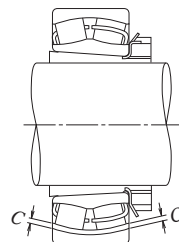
Medición del Juego de los Rodamientos de Rodillos Esféricos
